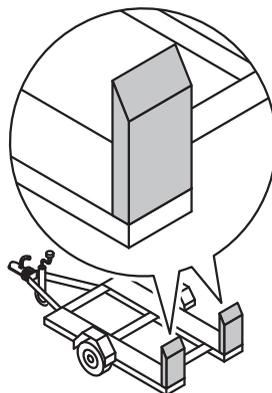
Rampe rabattable vers le haut (exemple remorque pour machines)
